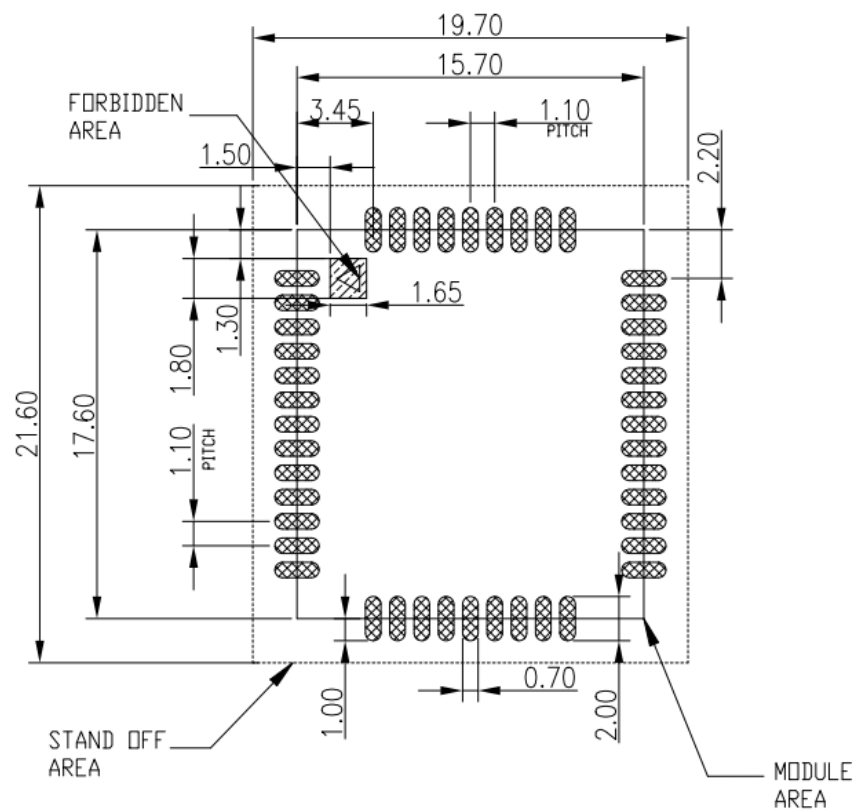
推荐 PCB 封装尺寸 (单位: 毫米)
